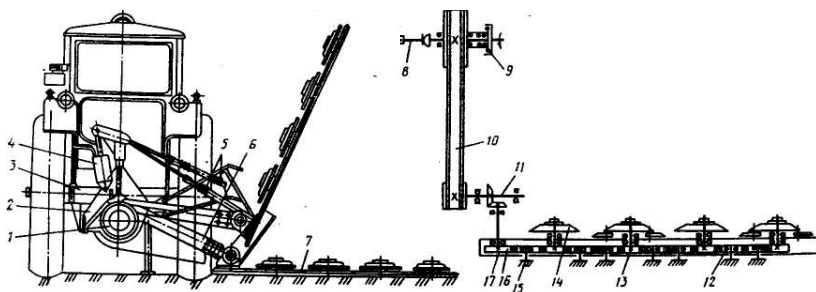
Четырехроторная косилка на базе колесного трактора: 1 – ременной привод; 2, 3 – кронштейны; 4 – гидроцилиндр; 5 – тяги; 6 – балка; 7 – режущий аппарат; 8 – карданный вал; 9 – центробежная обгонная муфта; 10 – ременная передача; 11 – конический редуктор; 12, 13 – зубчатые колеса; 14 – роторы; 15 – промежуточные шестерни; 16 – ведущая шестерня; 17 – вертикальный вал
